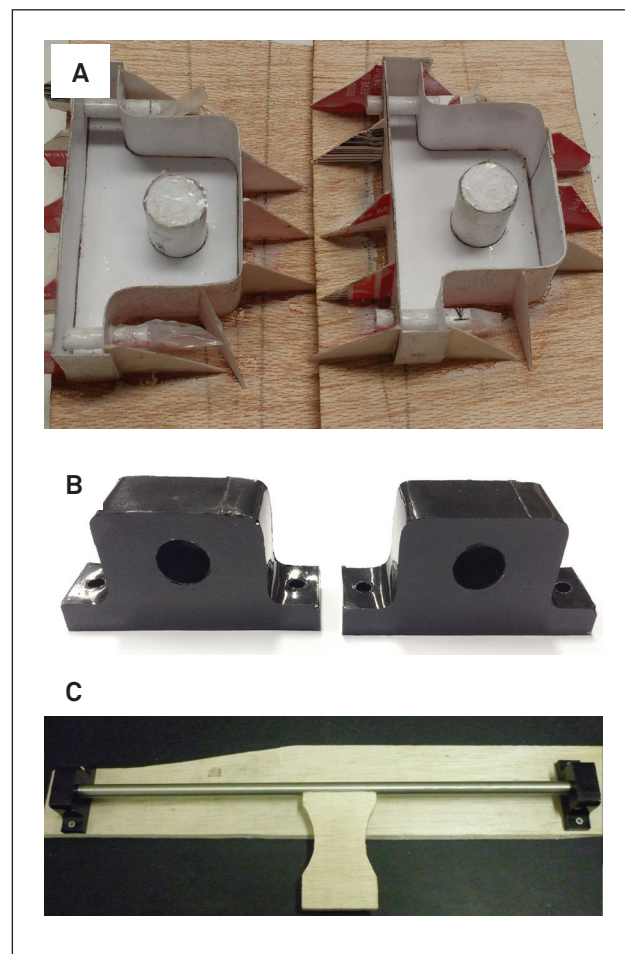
(A) molde dos mancais; (B) mancais desmoldados e (C) testes dos mancais.
